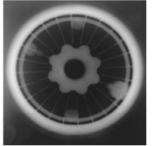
带内筋结构壳体部件 Fig. 6 Shell parts with internal reinforcement ribs
